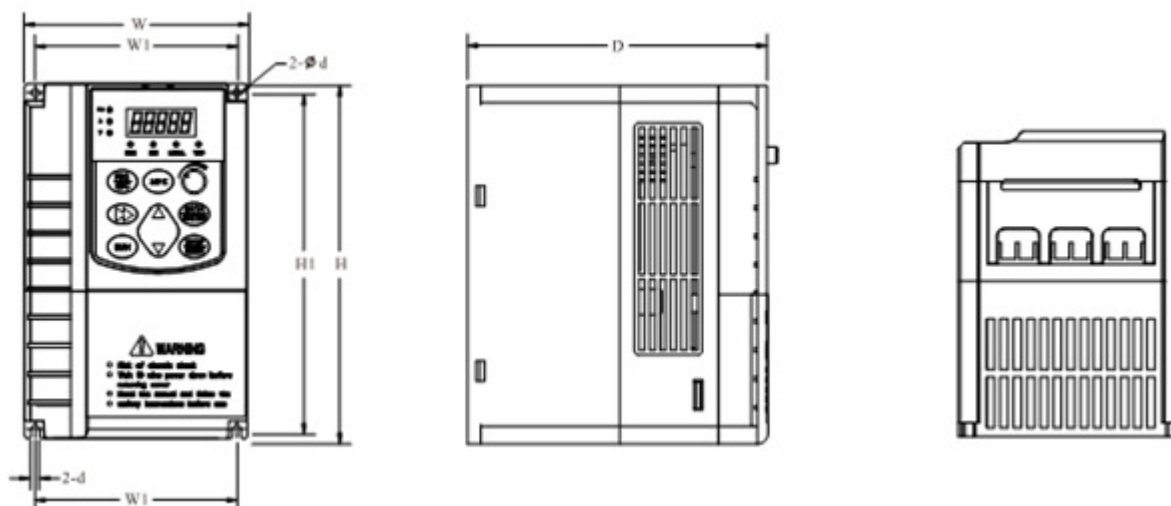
Внешний вид инвертора SL9 в пластиковом корпусе
